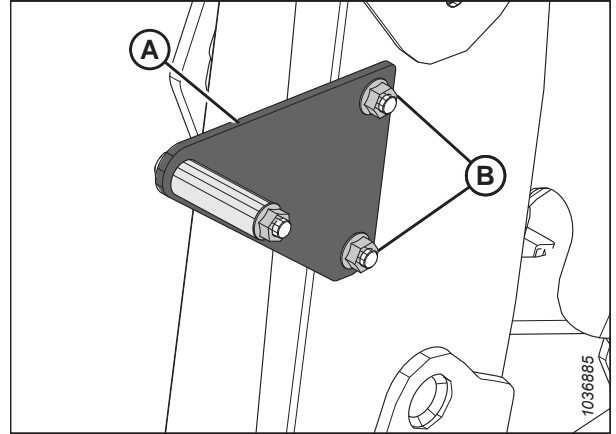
Кронштейн формовочного щитка — серия R
